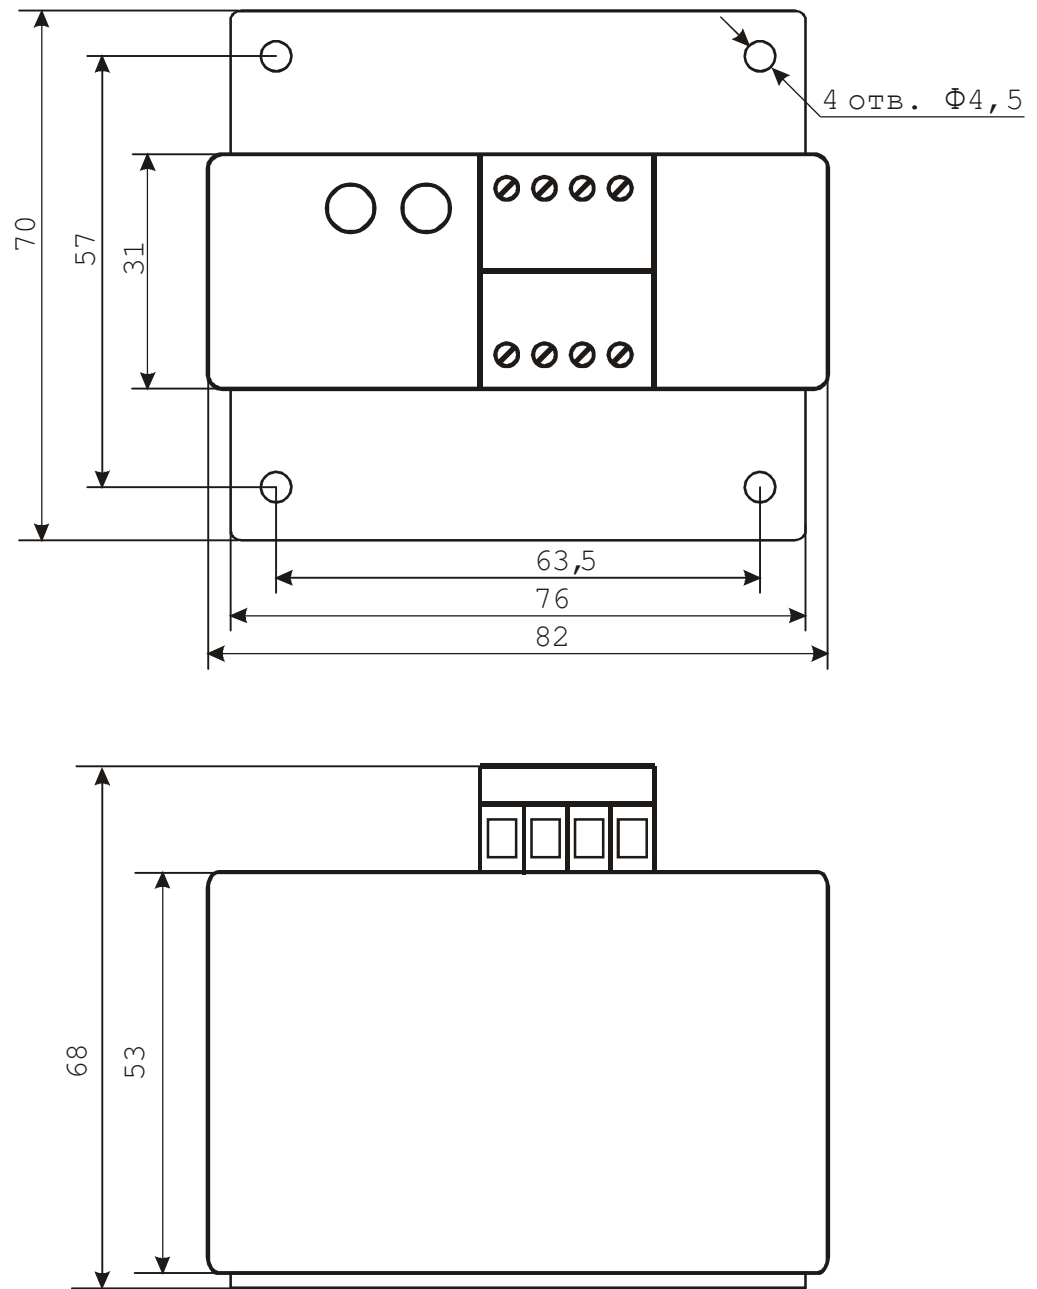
Габаритный чертёж ИП-40030-1-0-В4, ИП-40030-1-0-С4
